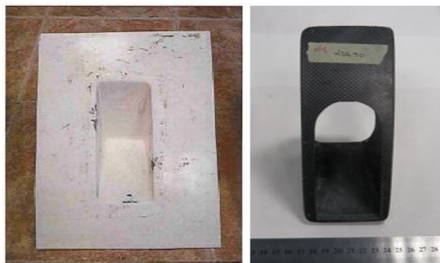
(Izq.) Molde y (Der.) escuadra de composite fabricada.
